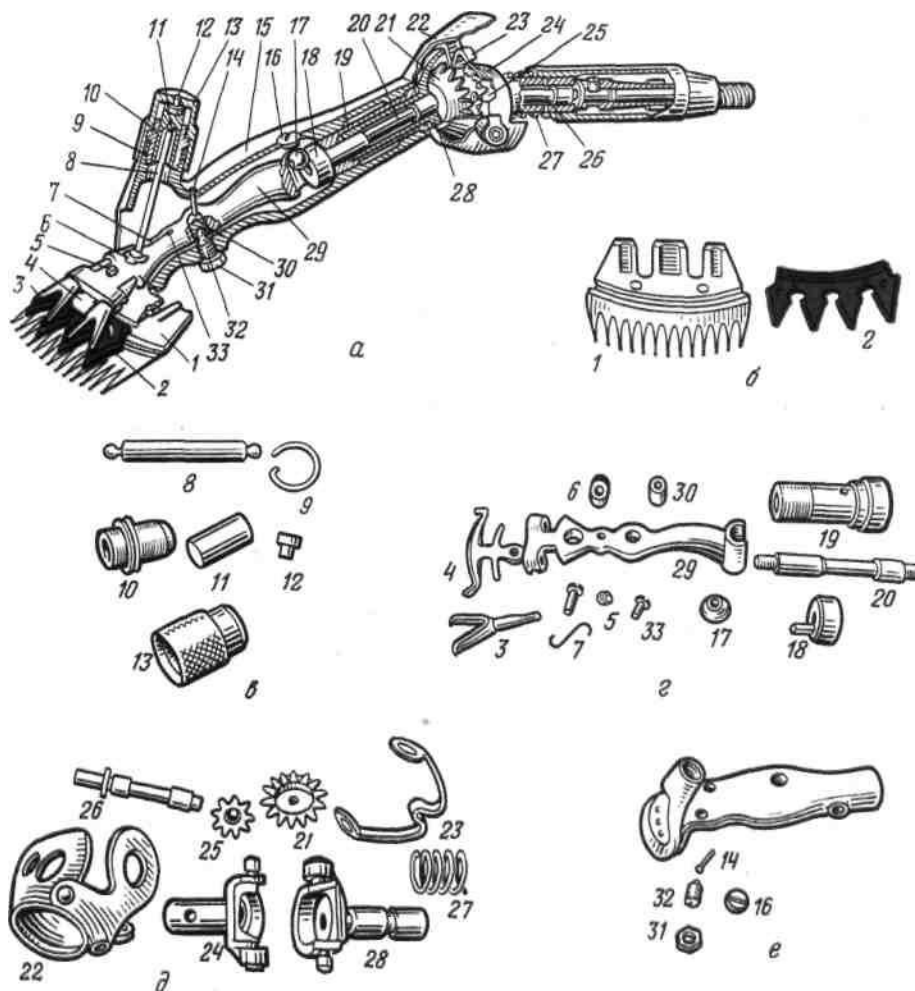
Общий вид (а) машинки МСО-77Б для стрижки овец и детали режущего аппарата (б), нажимного (в), эксцентрикового (г), шарнирного (д) механизмов
